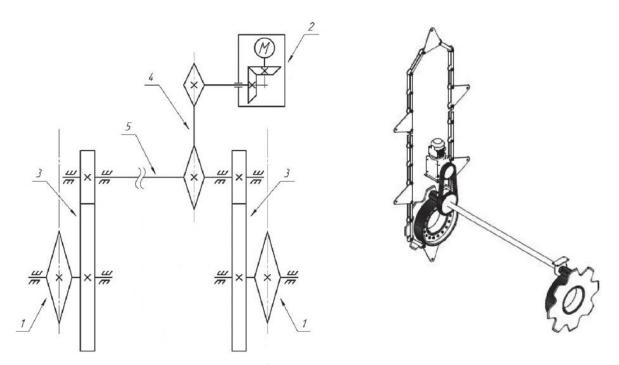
Кинематическа / реалистичная схема привода роторной автоматизированной парковки:
